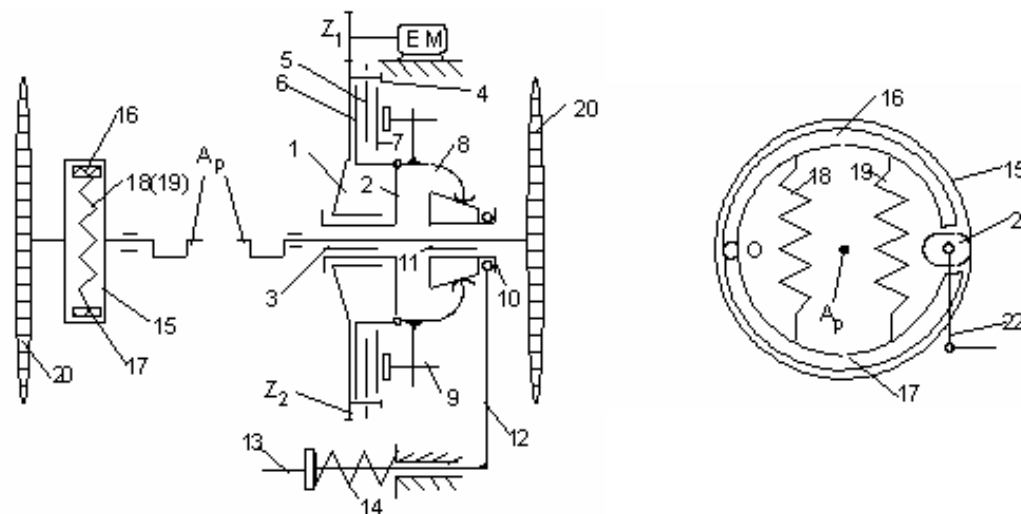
Mecanismul de acționare și frâna pe mașina de țesut Unirea tip A
